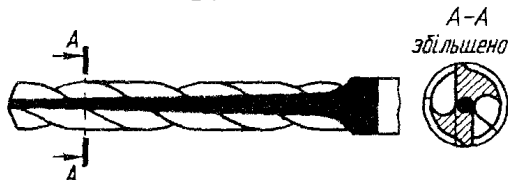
Стовщення перемички свердла для глибокого свердління в бік хвостовика
